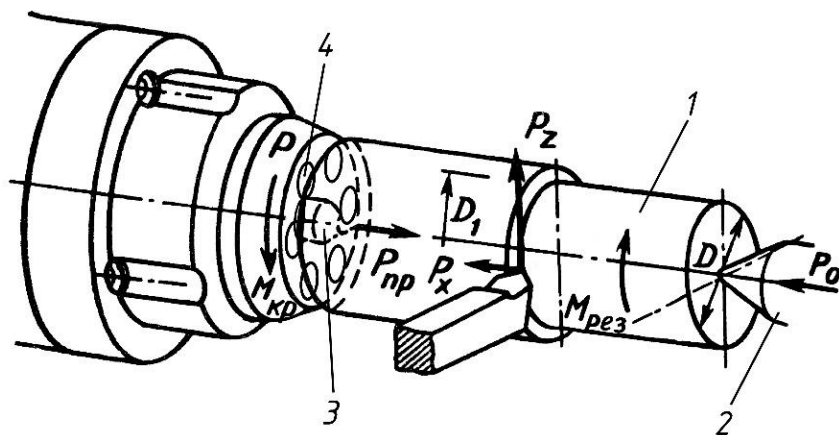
Схема сил, действующих на заготовку, закрепленную в штырьковом патроне
